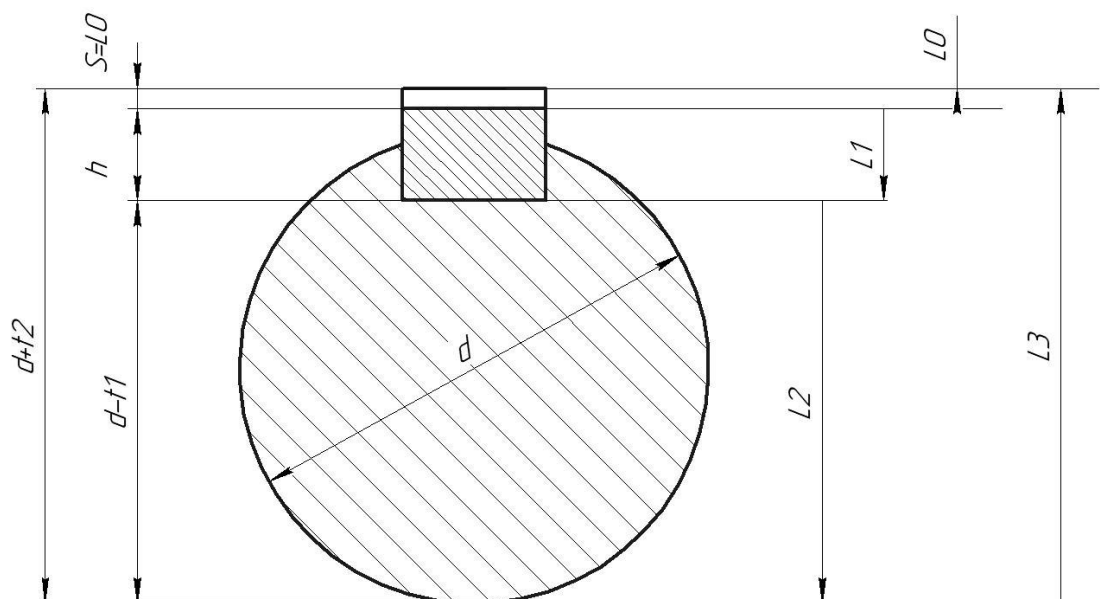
Ескіз шпонкового з'єднання з геометричною схемою розмірного ланцюга
